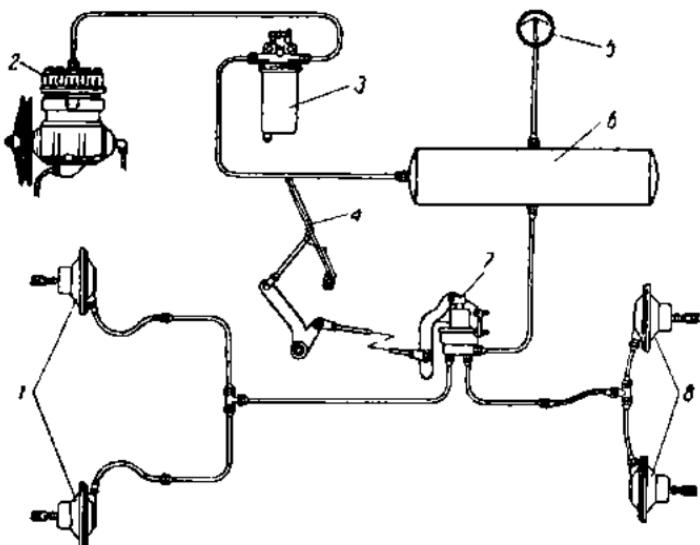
Схема тормозной системы. (1 и 8 — тормозные камеры; 2 — компрессор; 3 — фильтр; 4 — тормозная педаль; 5 — манометр; 6 — рессивер; 7 — тормозной кран).
